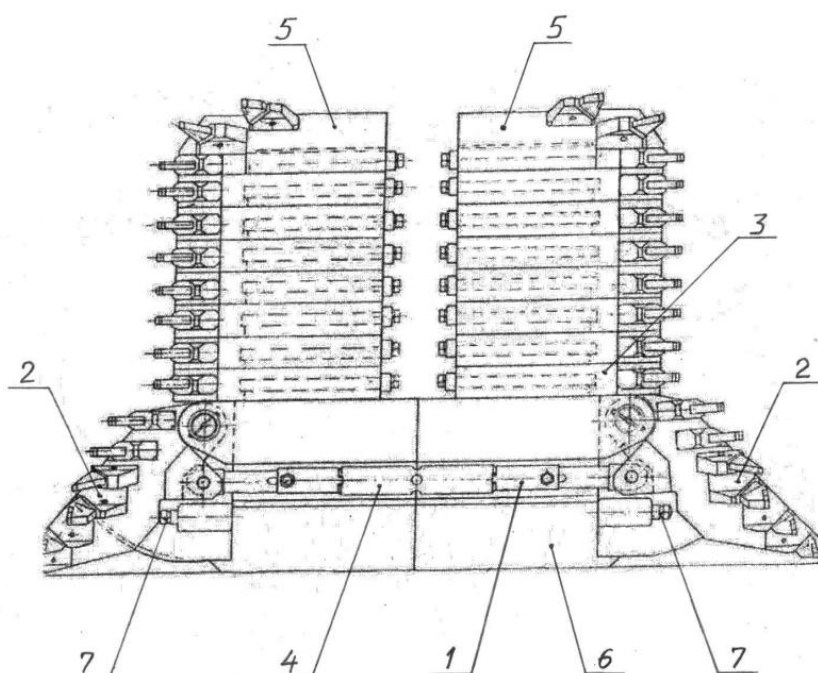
Исполнительный орган с принудительным отводом нерабочей группы резцов:
